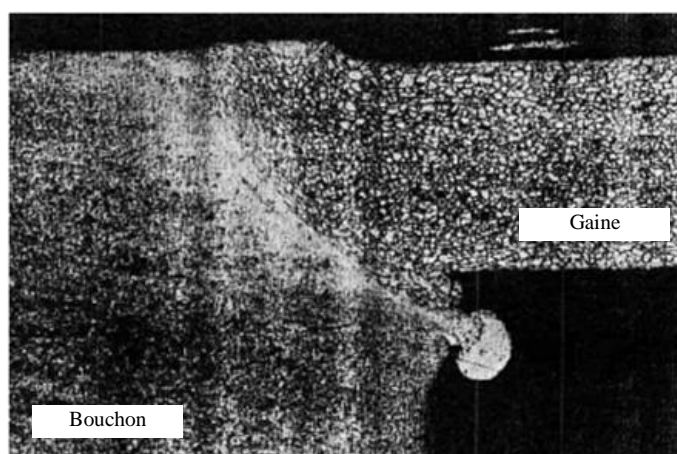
Macrographie de soudure par résistance d'un alliage DT2906 [80] (échelle non communiquée)
